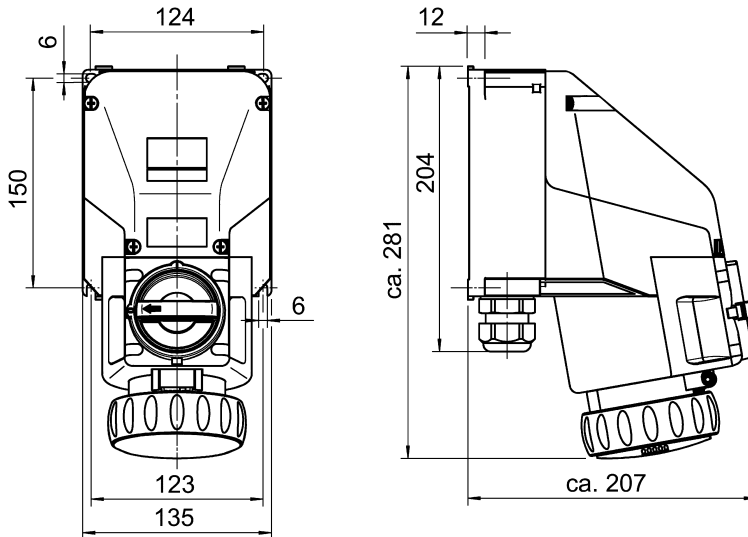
Maßzeichnung Typ 7571/11-4.. und Typ 7571/11-5..
